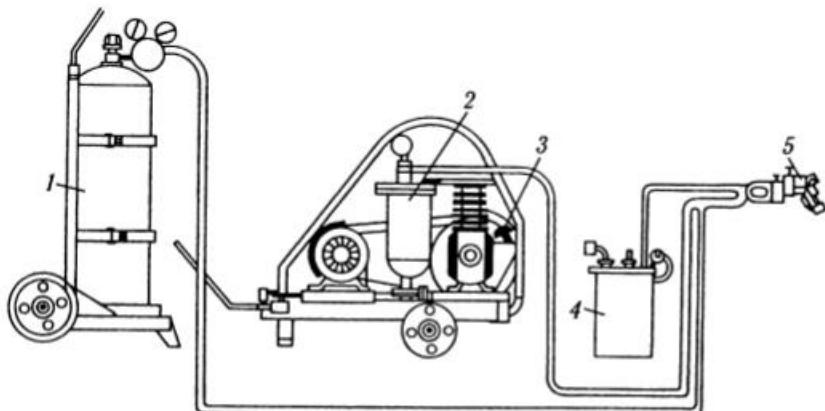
Універсальний пересувний агрегат для металізації:
